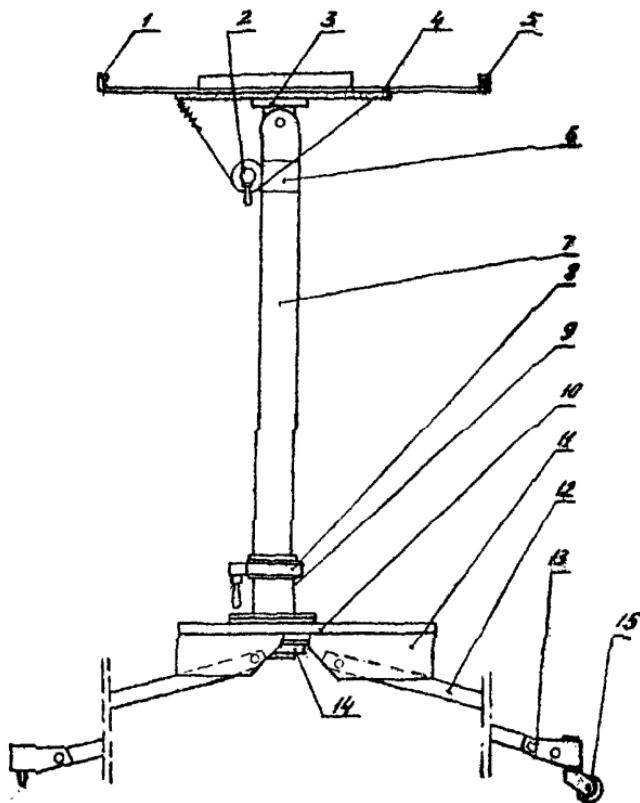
Рис. I. Штатив для установки дефектоскопов: I,5 - упор; 2 - фиксатор; 3 - стойка; 4,10 - основание; 5,9 - хомут; 7 - труба; 8 - хвостик; 11 - скоба (алюминий); 12 - ножка; 13 - опора; 14 - гайка; 15 - ролик.
